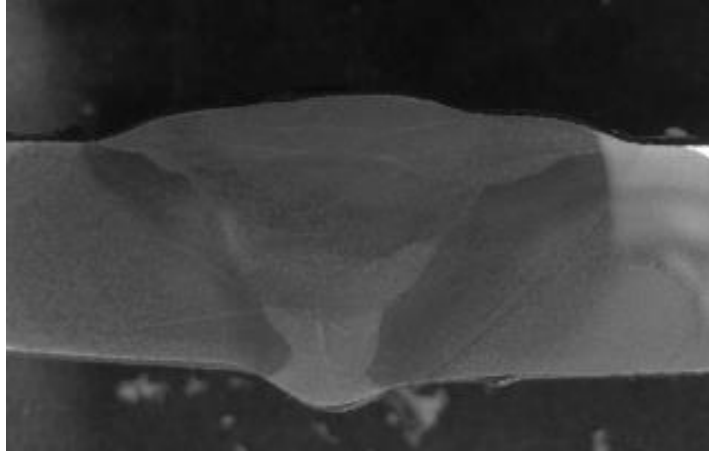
Photographie de la soudure attaquée au Nital.
